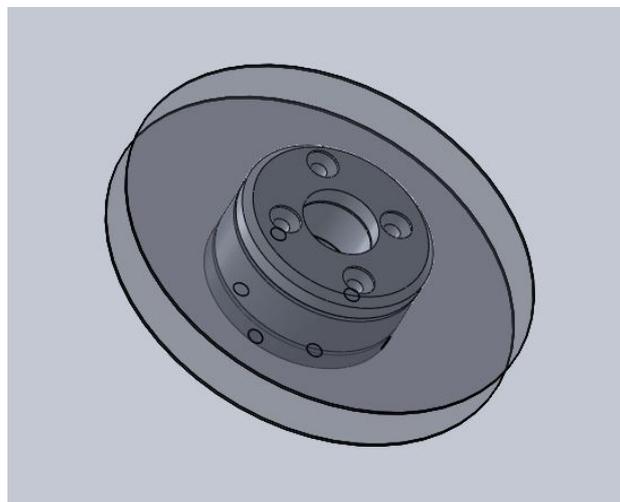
Conjunto ensamblado de cuchillas. Fuente: modelado 3D de la máquina
